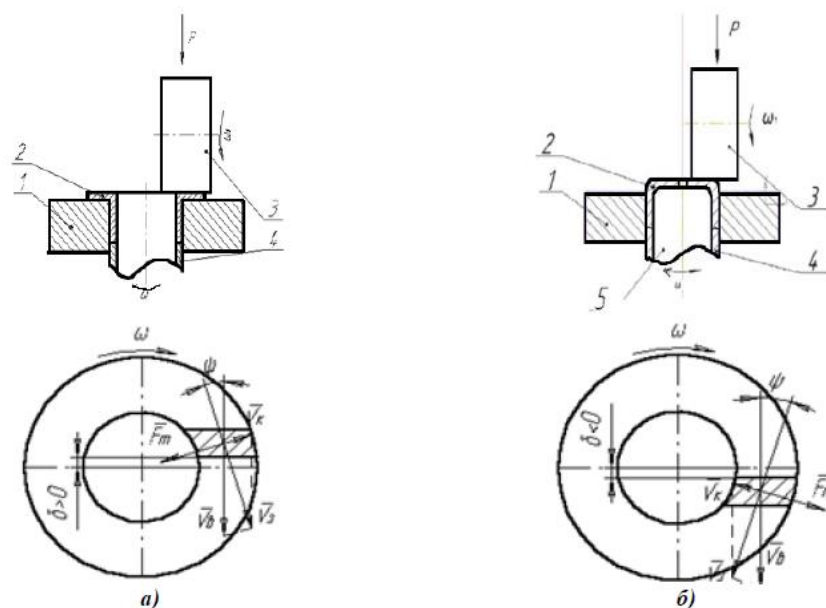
Залежність положення кута ψ між проекціями векторів швидкості точок інструменту і заготовки на площину при торцевому обкочуванні кільцевої заготовки циліндричним валком, від напрямку зсуву валка δ
